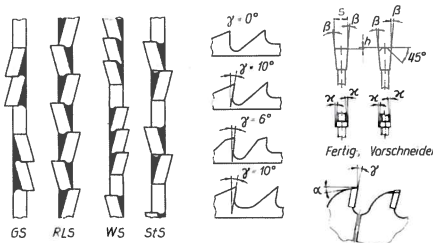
Zahnformen für Sägewerkzeuge (Sägebänder und Kreissägeblätter) zur Aluminiumzerspannung
